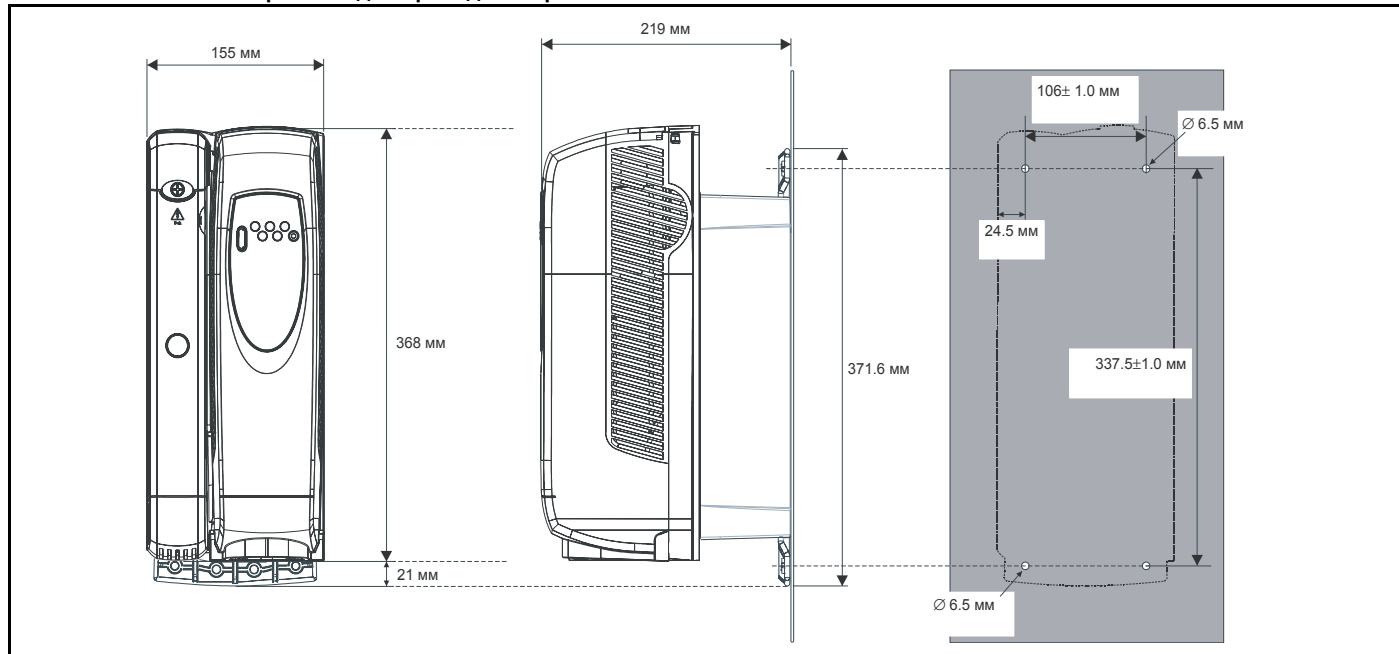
Монтаж к поверхности для привода габарита 3
